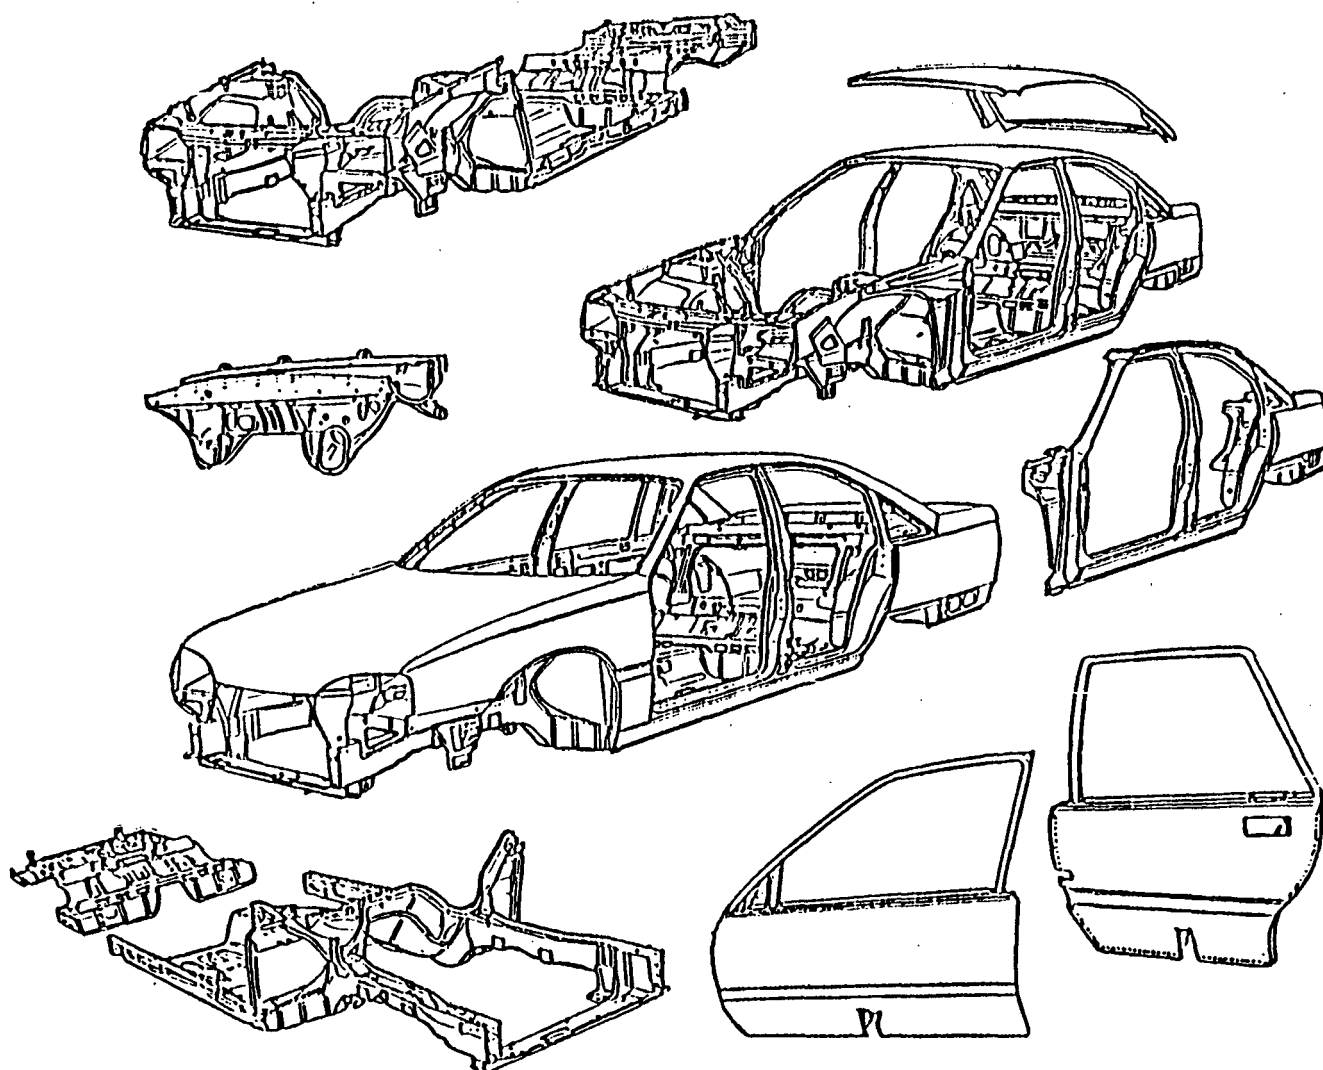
Exemplo típico de soldagem automática de chapas finas, a ponto.
